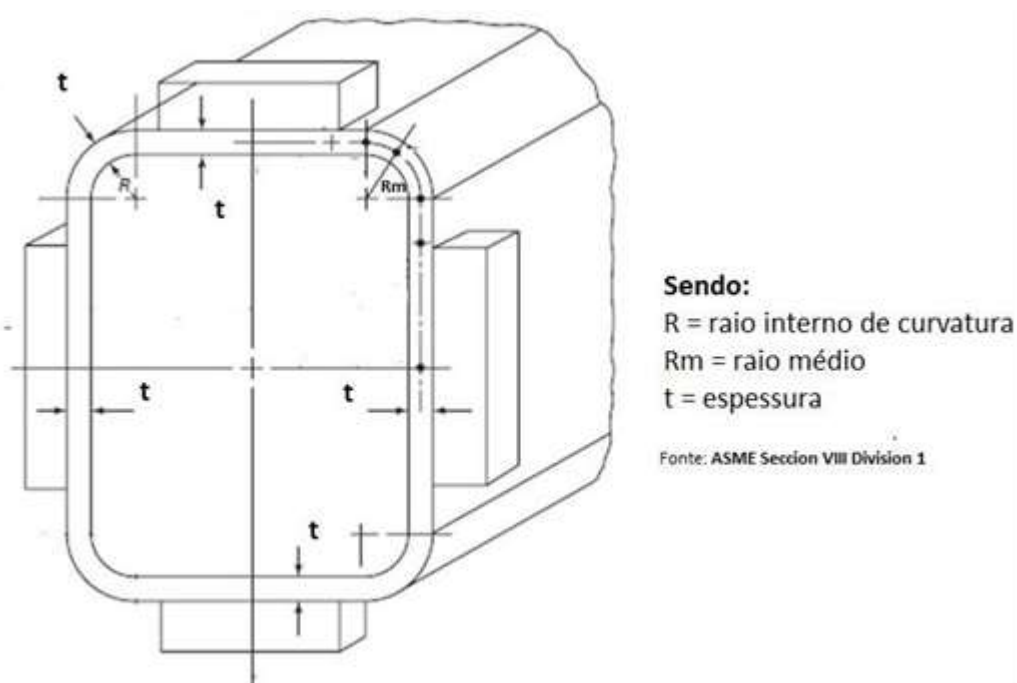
Vaso de pressão de secção retangular com reforço estrutural externo [Adaptado do código ASME VII divisão 1, Ed. 2010]
